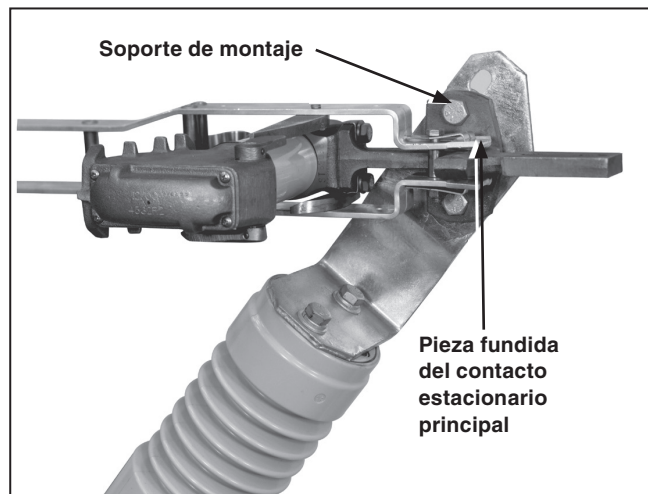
Ajuste la posición de la pieza fundida del contacto estacionario principal.
